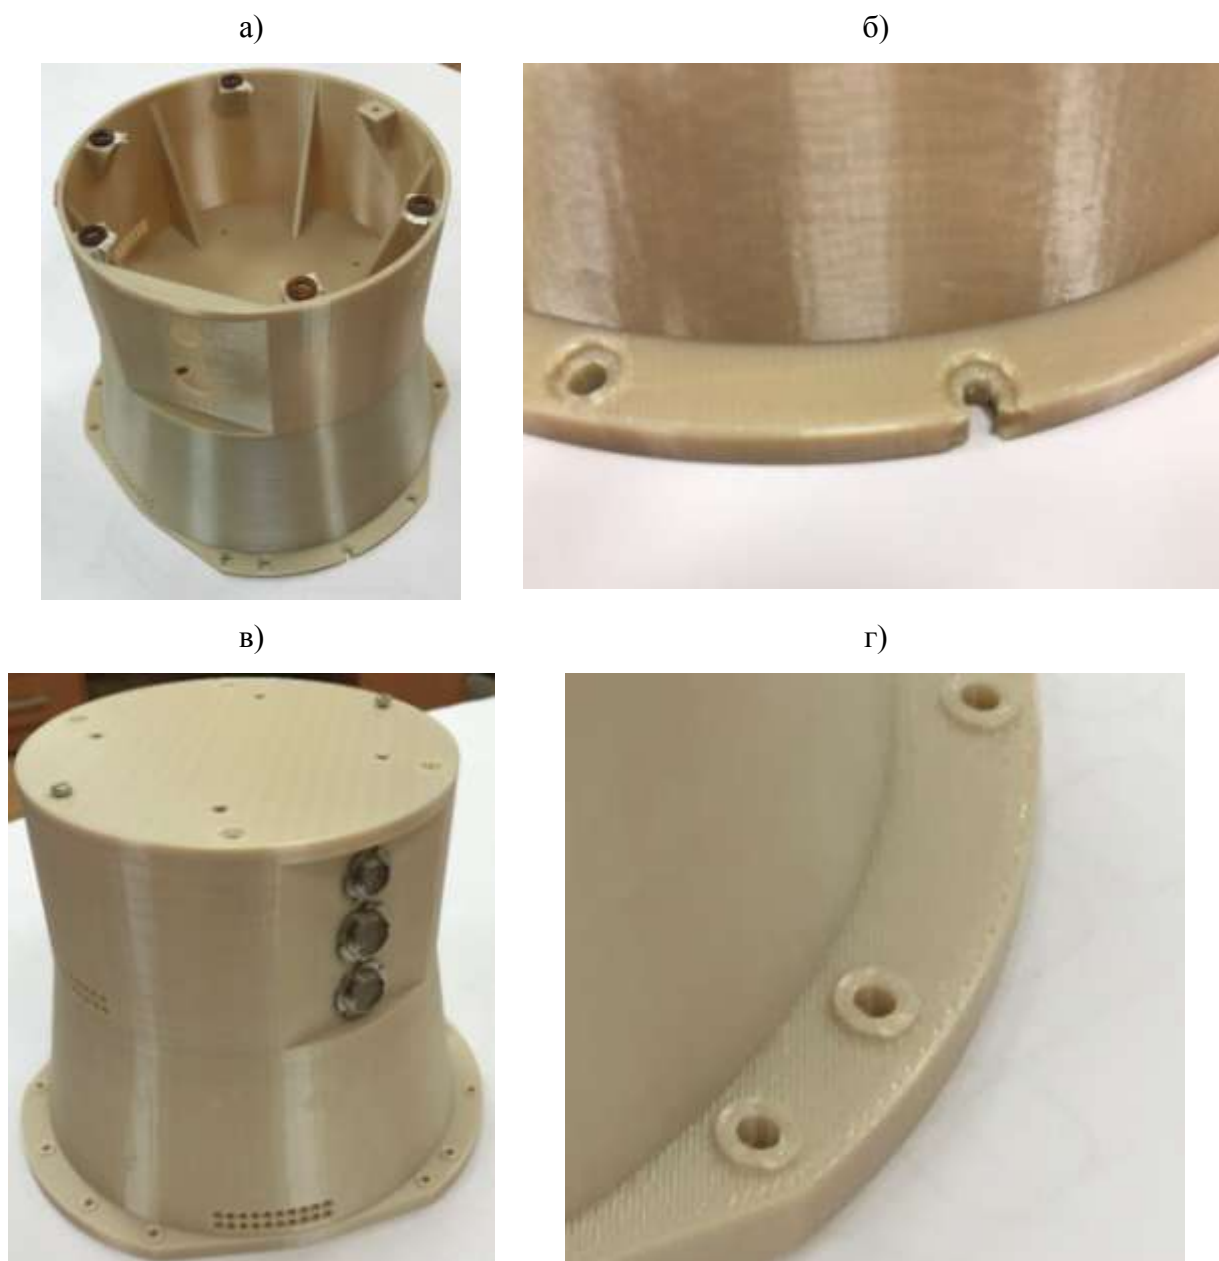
Детали корпуса электроники V1; а) – общий вид детали; б) – место разрушения корпусной детали корпуса электроники V1; в) – общий вид корпусной детали V1.1; г) – усиленные места закрепления корпусной детали V1.1
